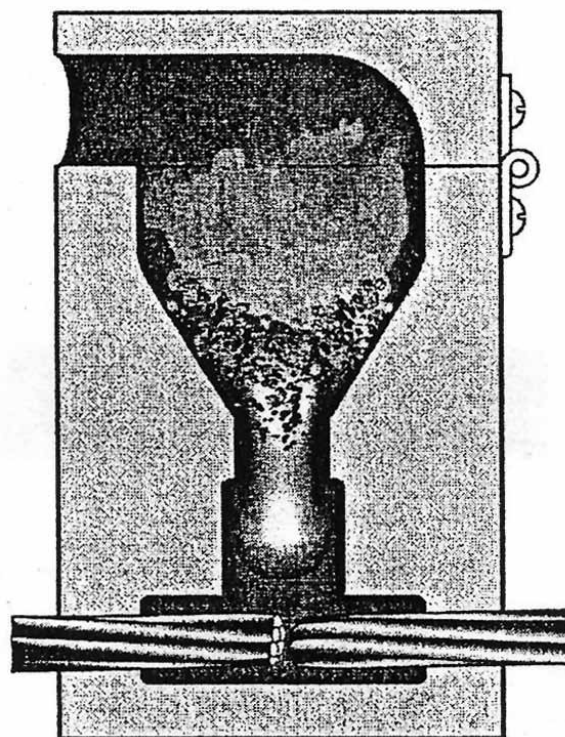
Colada del material fundido sobre las piezas a soldarse
